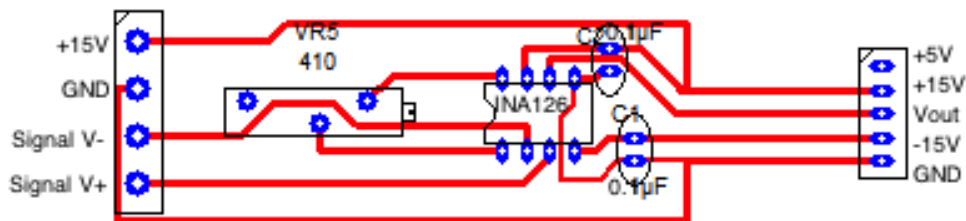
PCB de la tarjeta CAS sensor de presión diferencial para determinar nivel de agua.
